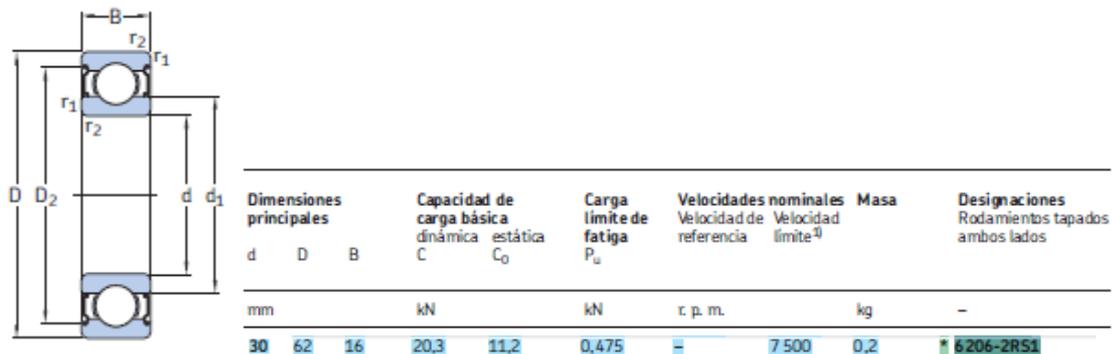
Dimensiones y características del rodamiento sellado 6206-2RS.
